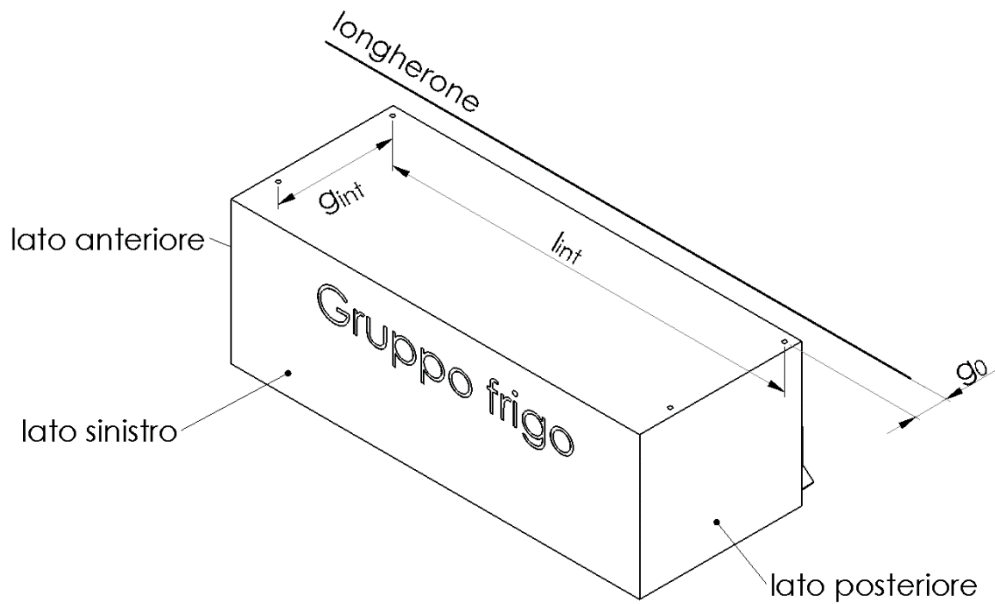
c Quote e dimensioni dei gruppi frigo
